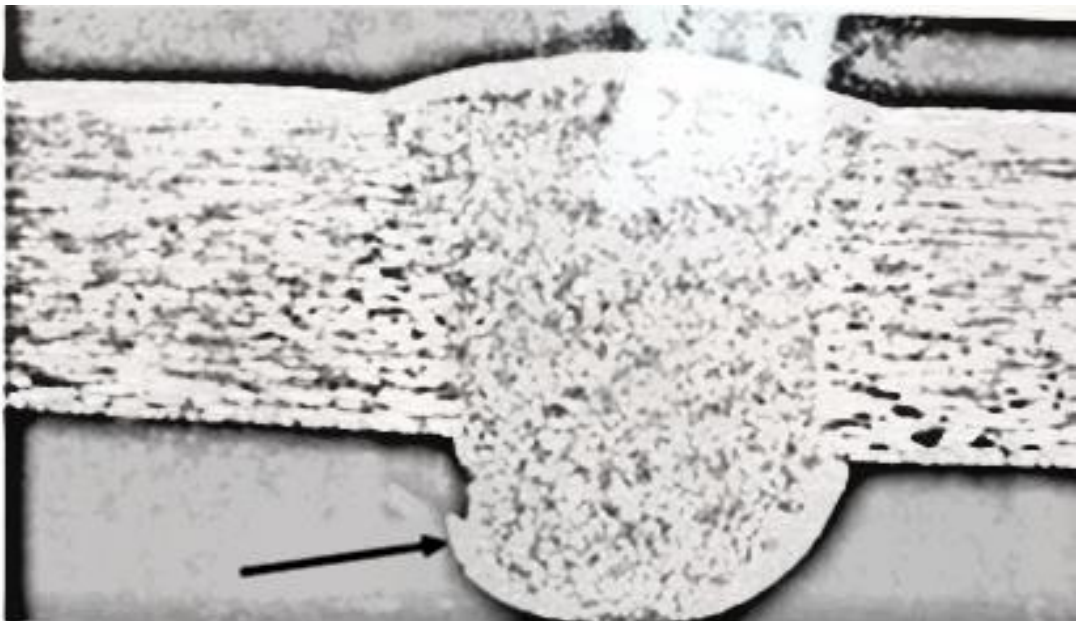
Макроструктура сварного шва (проплав)
